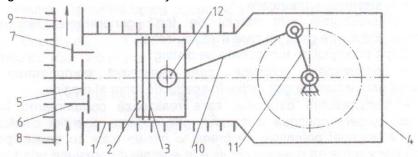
Schema constructivă a unui compresor cu piston:
